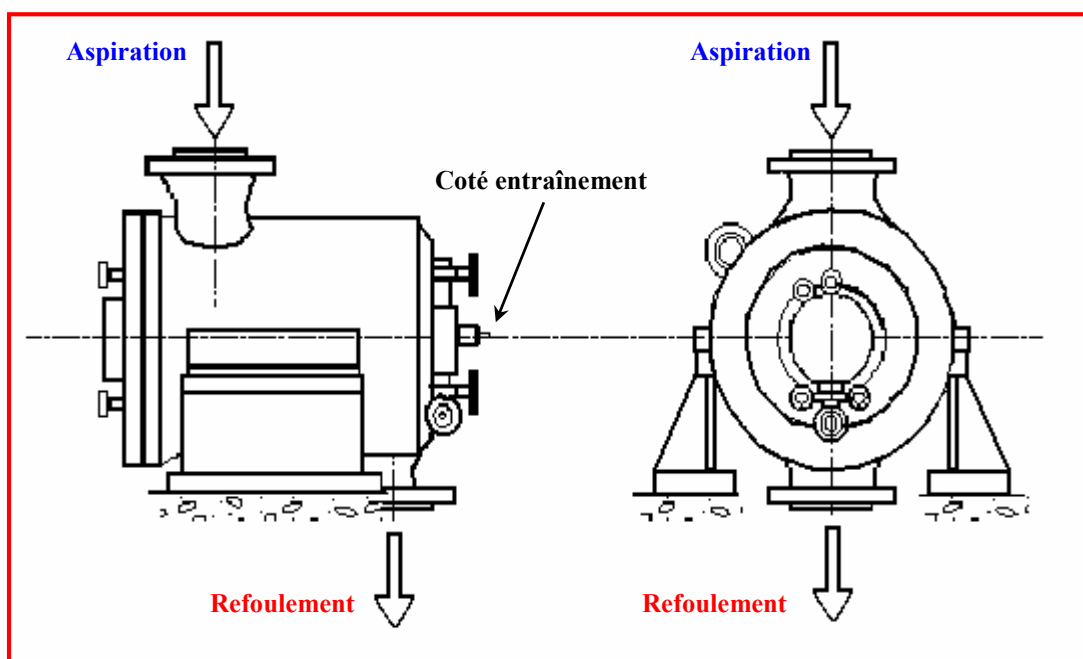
Compresseur à plan de joint vertical (Type Barrel).
